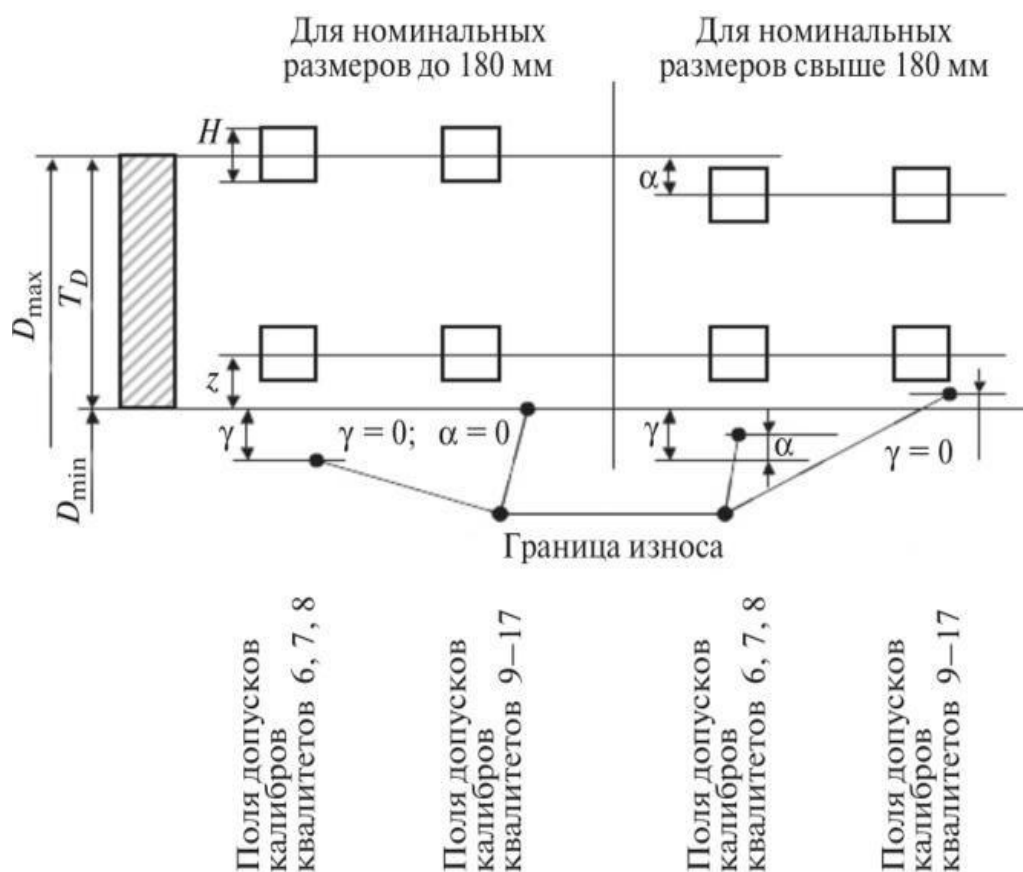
Расположение полей допусков калибров и для контроля отверстий
